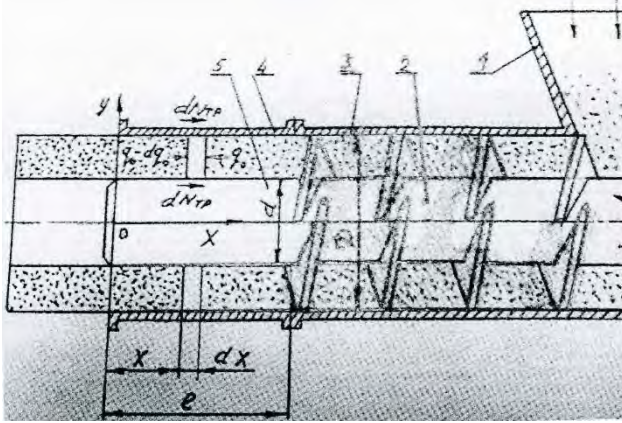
Шнековый пресс с цилиндрической формирующей головкой.
